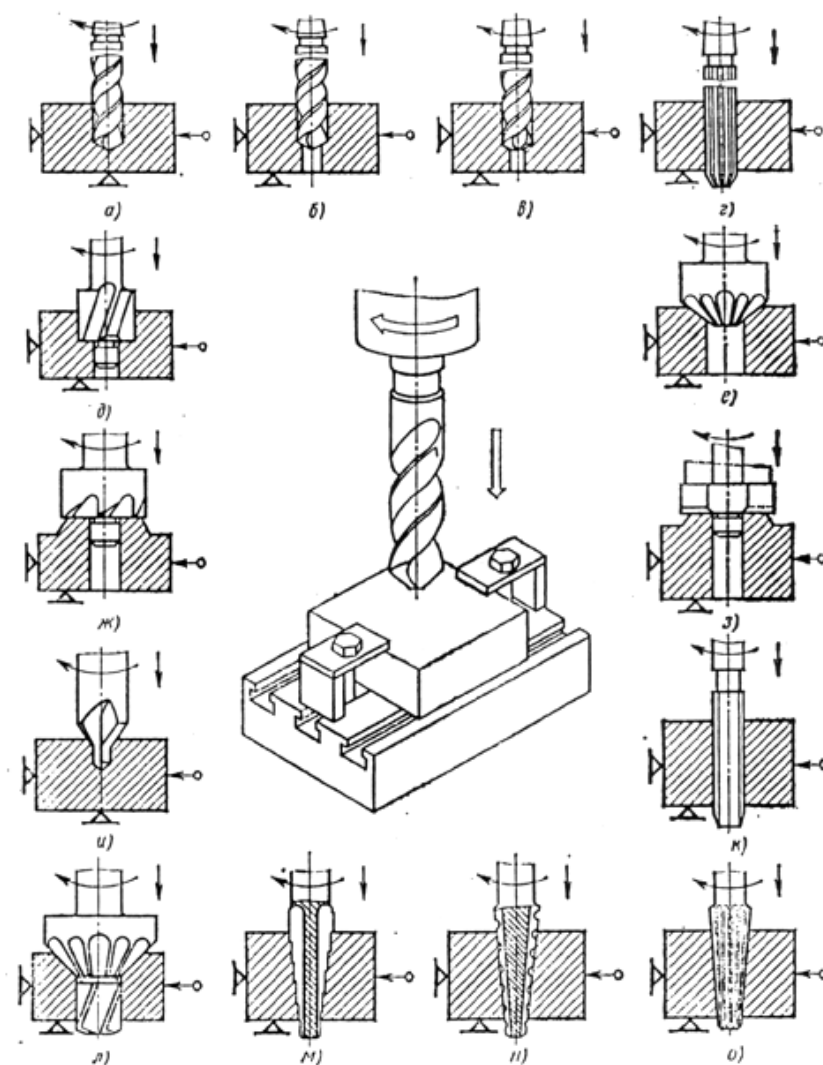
Схемы обработки поверхностей на сверлильных станках
